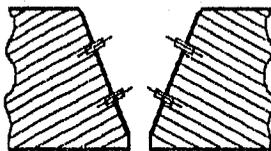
Tornillos colocados para anclar la soldadura en el metal base.
